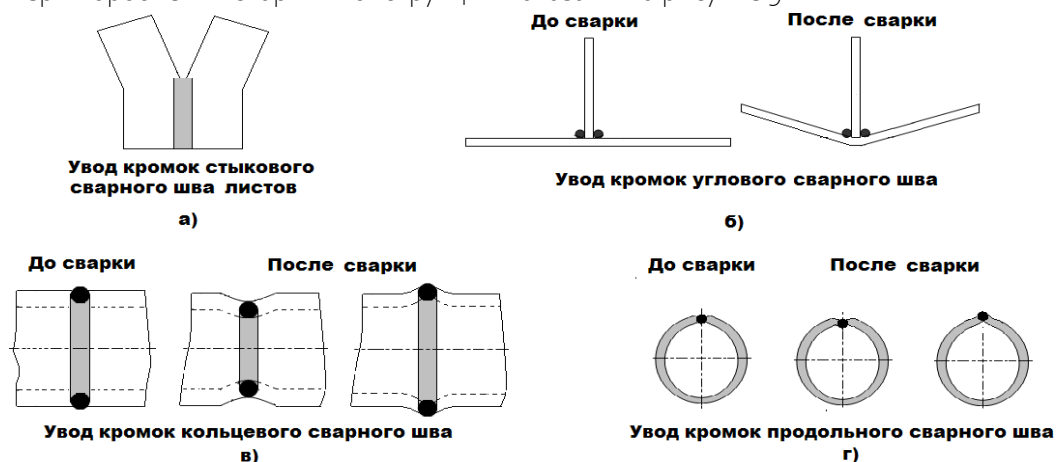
Коробление сварных конструкций: а – при сварке стыковых швов листов; б – при сварке угловых швов листов; в, г – при сварке оболочковых конструкций.
